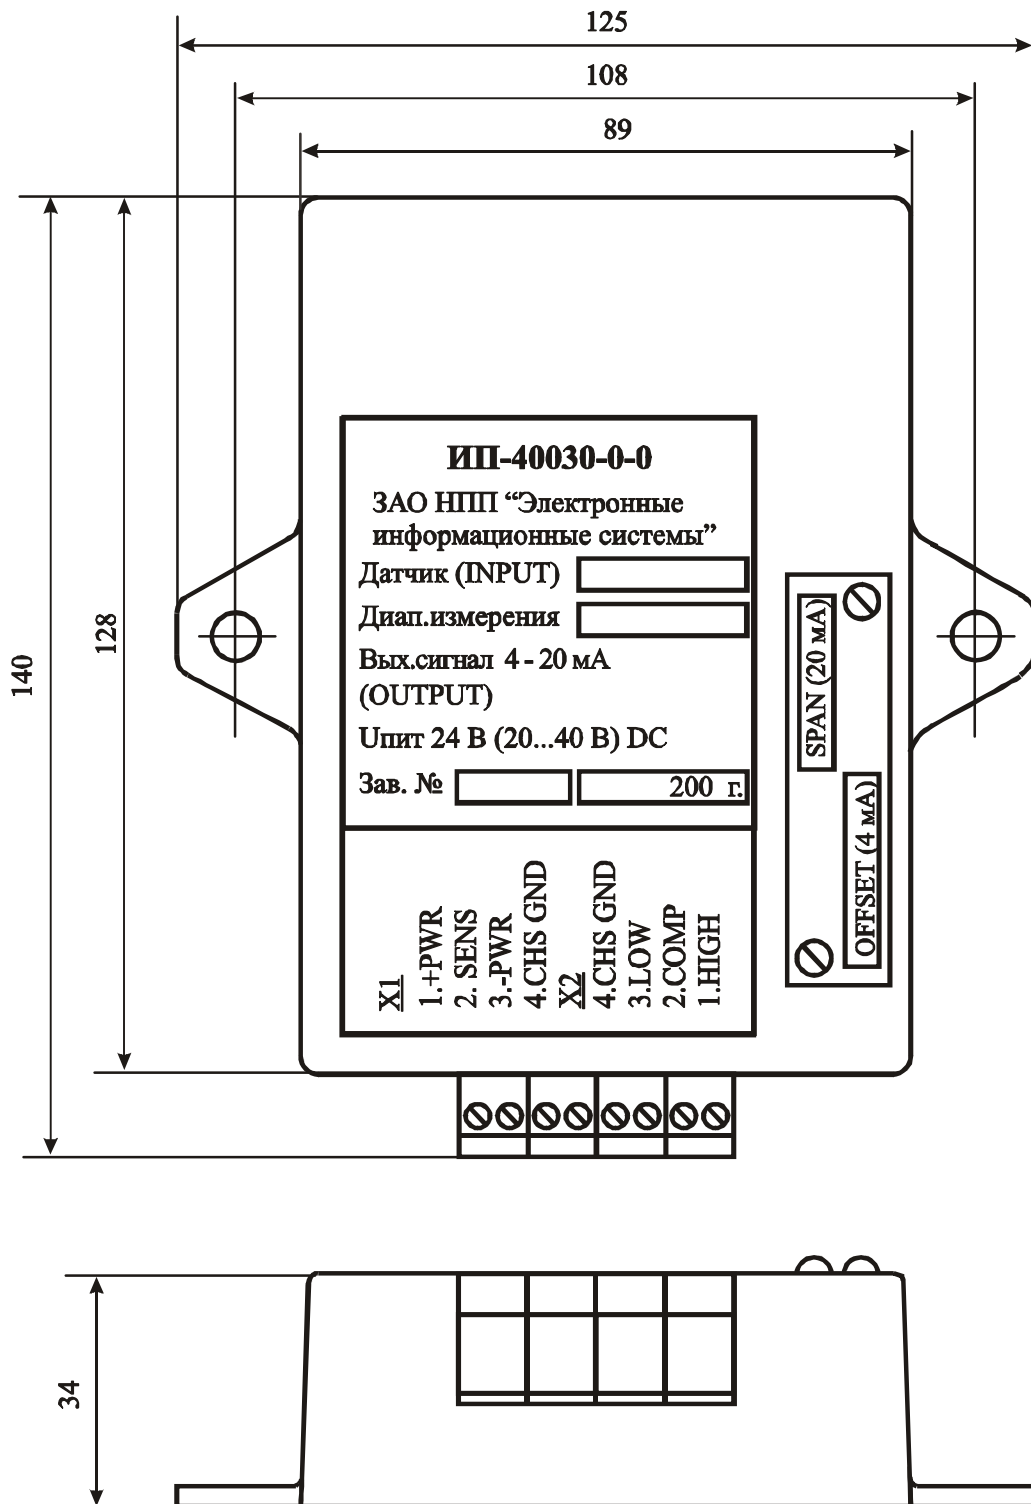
Габаритно-установочный чертёж ИП-40030-0-0-В4, ИП-40030-0-0-С4
